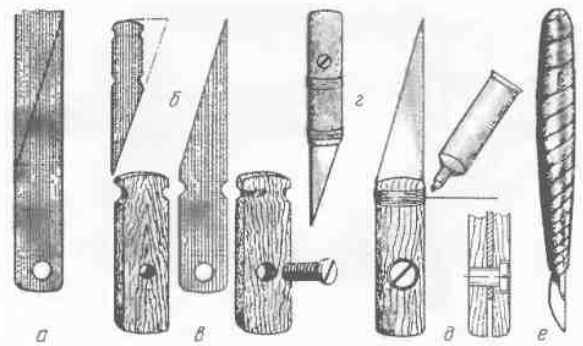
Изготовление двух ножей из полотна пилы для металла: а — линия разреза на полотне; б — заготовки для ножей; в — соединение половинок ручки с ножом; г — крепление ручки маленького ножа; д — крепление ручки большого ножа обмоткой нитью на клею и винтом; е — ножичек из обломанного плоского надфиля с обмоткой ручки изоляцией
